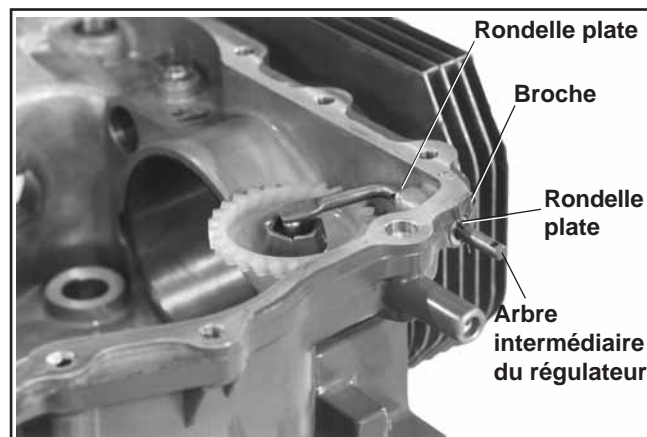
Dépose de l'arbre intermédiaire du régulateur.
